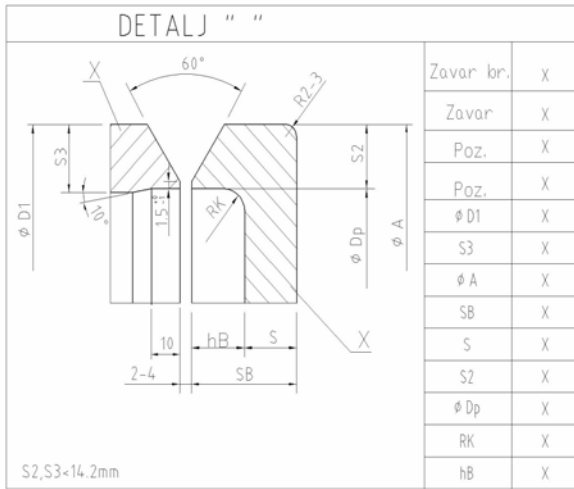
Detalj žlijeba za zavarivanje odzrake - odvodnje i komore
